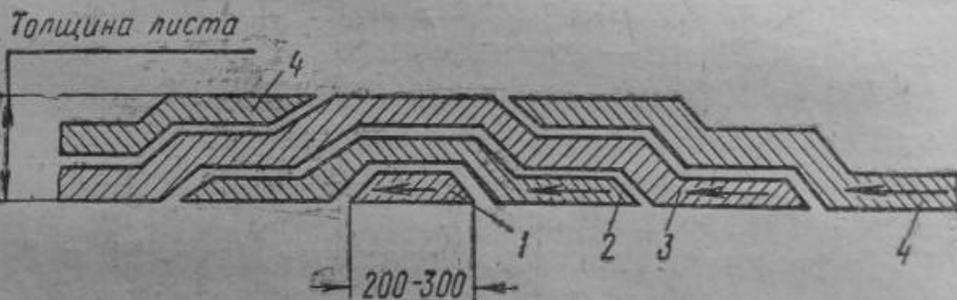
Схема сварки длинных многослойных швов «горкой»:
